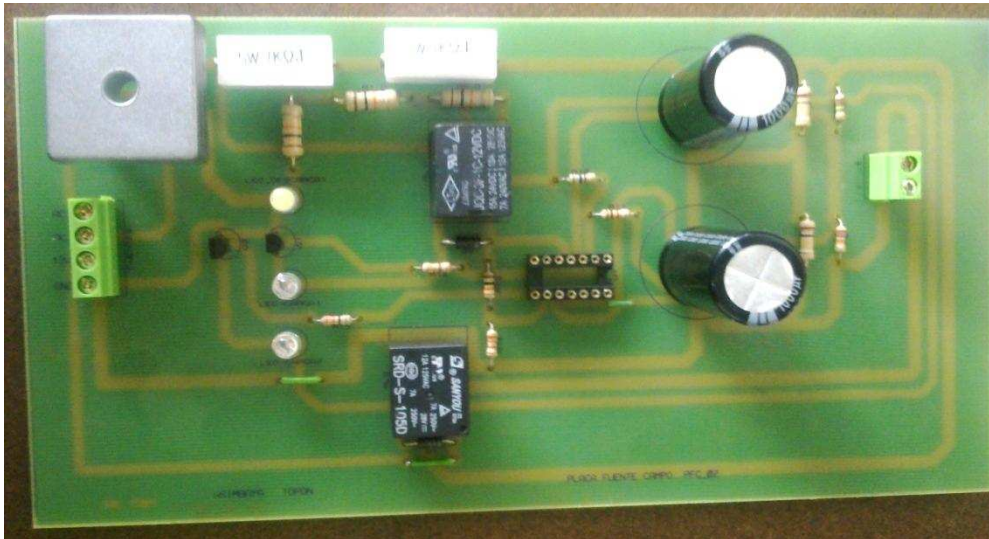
4 Tarjeta Ensamblada de la Fuente de Campo
